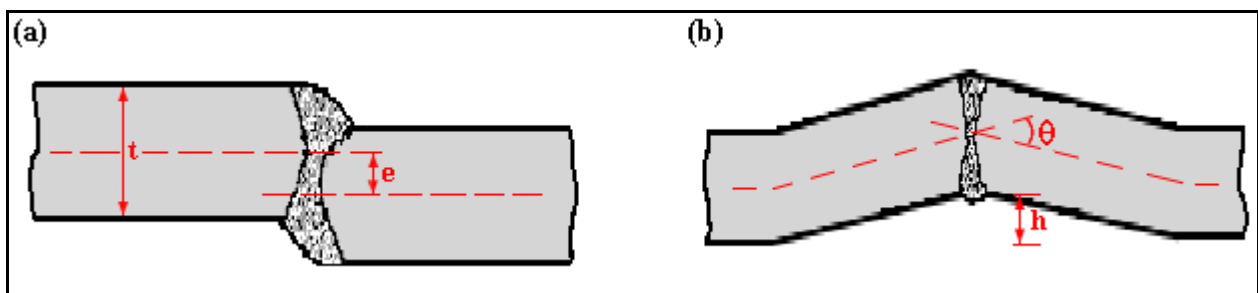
Juntas desalineadas soldadas a tope. (a) Desalineamiento axial, y (b) angular.
